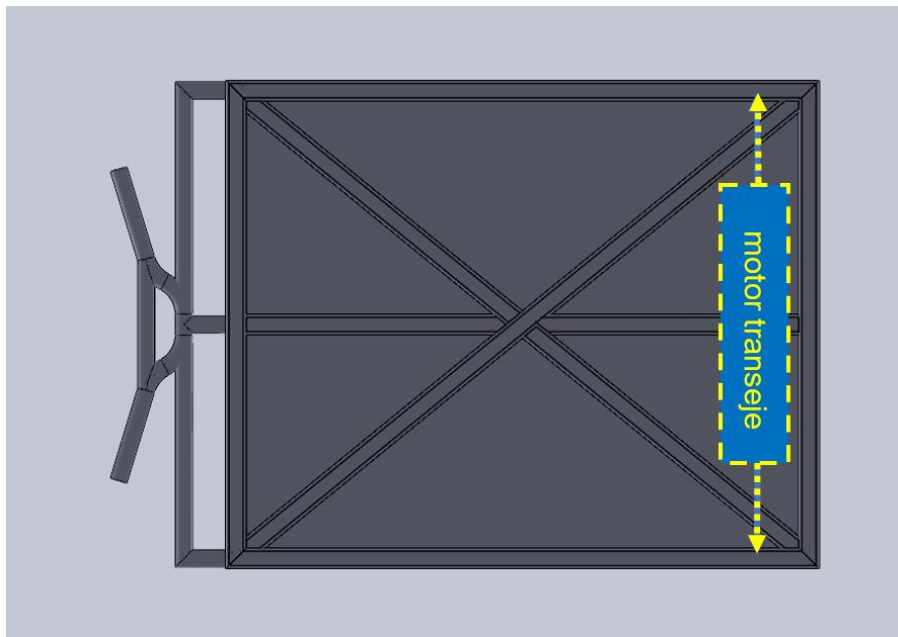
Disposición motorreductor transeje [fuente propia]
